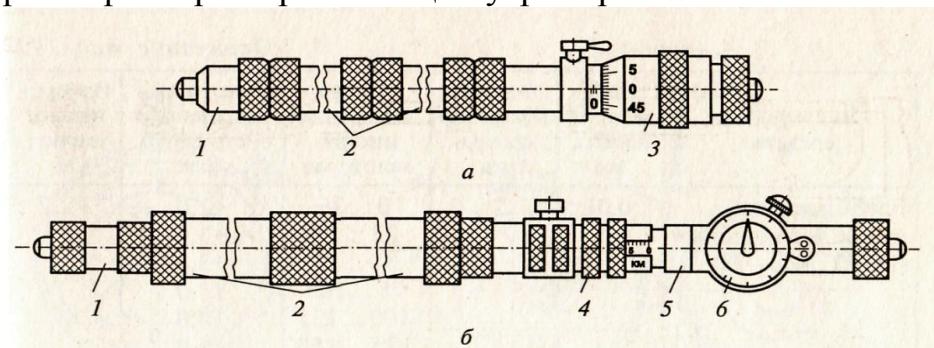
Измерение размеров при помощи нутромера; 1 — измерительные наконечники; 2 — удлинители; 3 — шкала; 4 — кольцо микроподачи; 5 — корпус; 6 — индикатор
